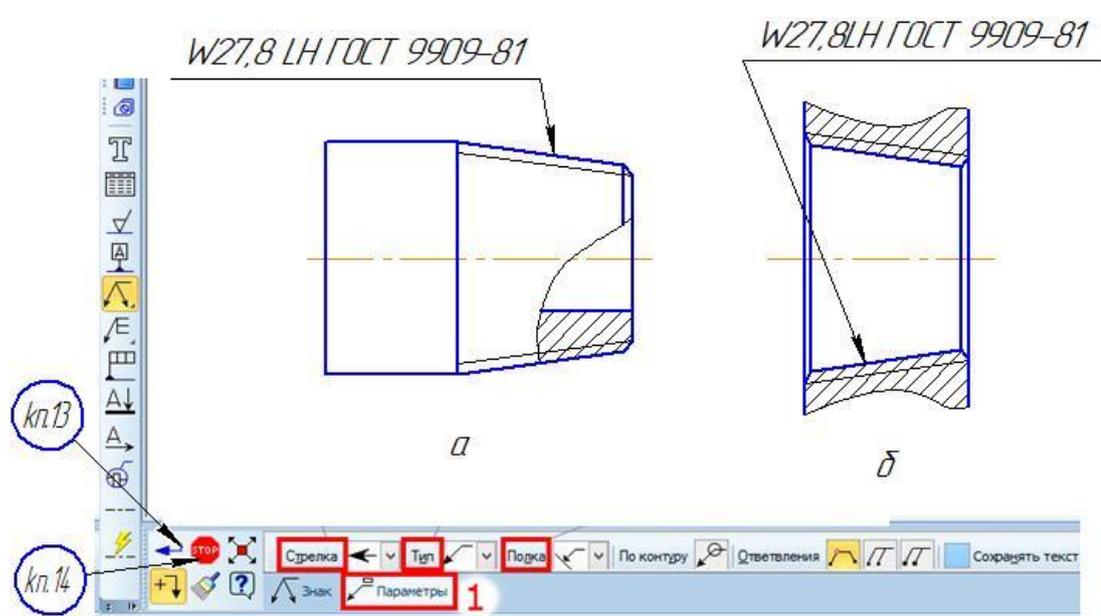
Обозначения наружной и внутренней конической резьбы вентиляй и баллонов для газа
